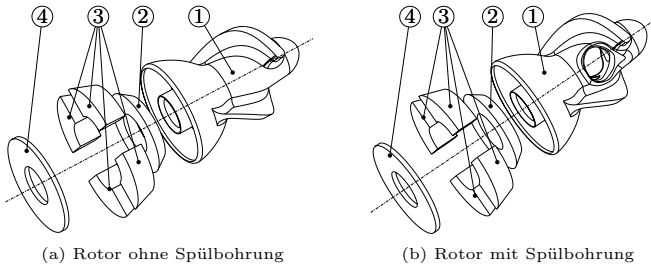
Explosionsdarstellung ebener Spiralrillenlager-Varianten: (1) Rotor ohne/mit Spülbohrung, (2) magnetischer Rückschluss, (3) Magnetsegmente, (4) ebene, ungerillte Spurscheibe
